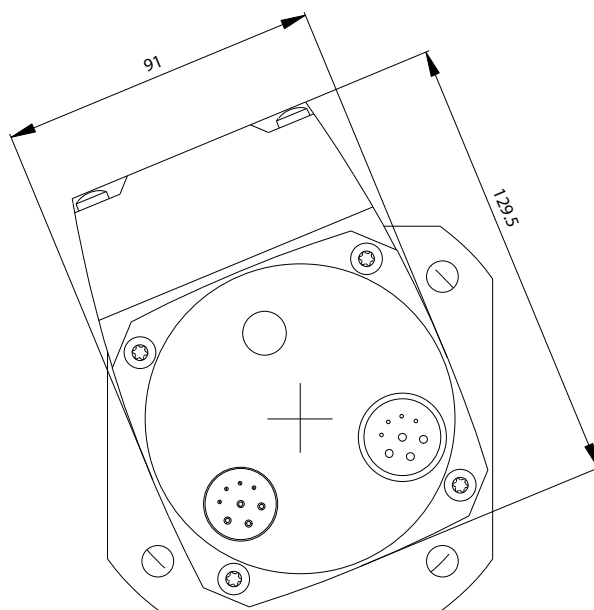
Seitenansicht: Servomotor mit IEC Flansch, ohne Bremse
